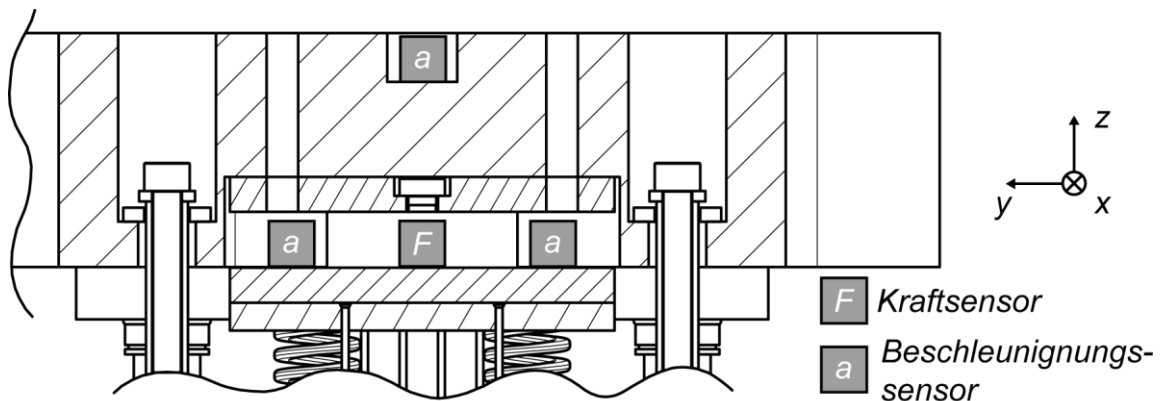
Positionen der Sensoren im Werkzeugoberteil
